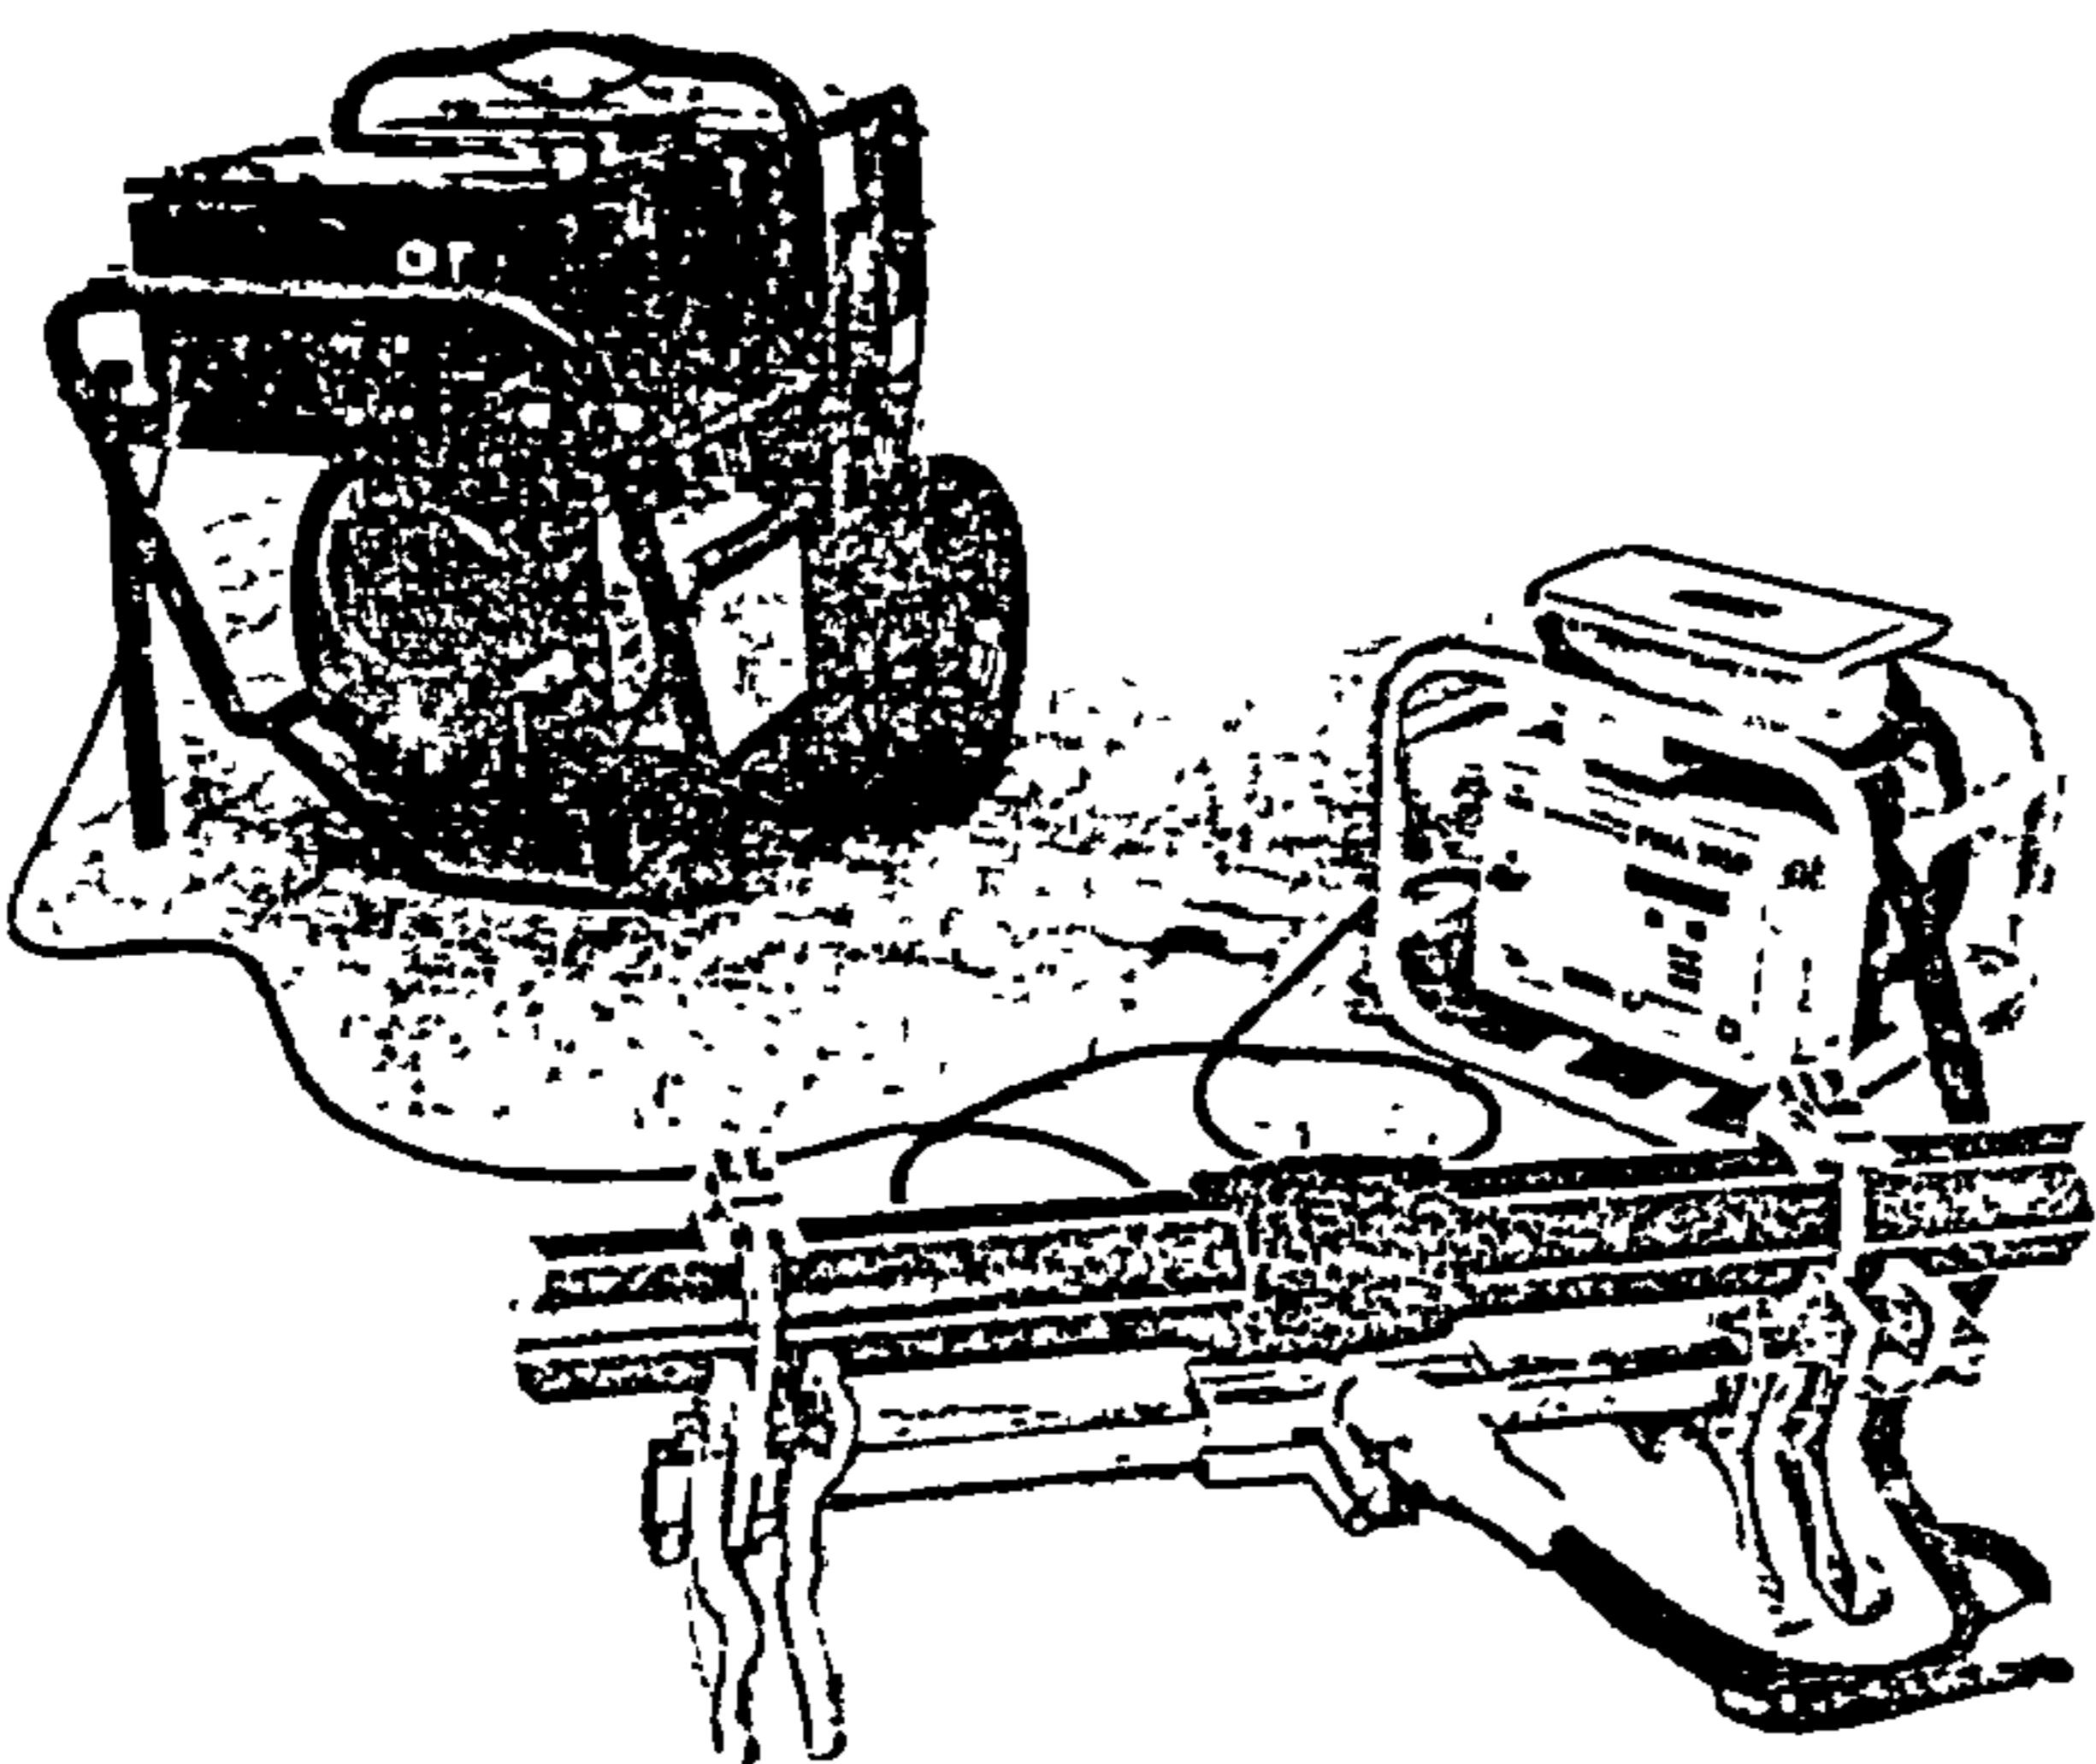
Размещение оборудования при сварке с помощью муфт с закладными нагревателями
